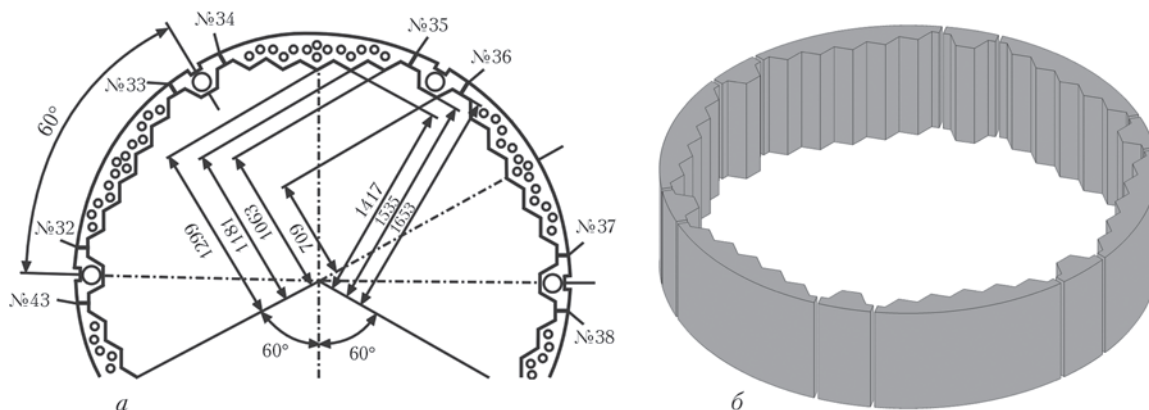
Центральное кольцо выгородки: а — чертеж сечения из паспорта изделия с расположением сварных швов № 32–43; б — сегменты кольца выгородки перед электрошлаковой сваркой
